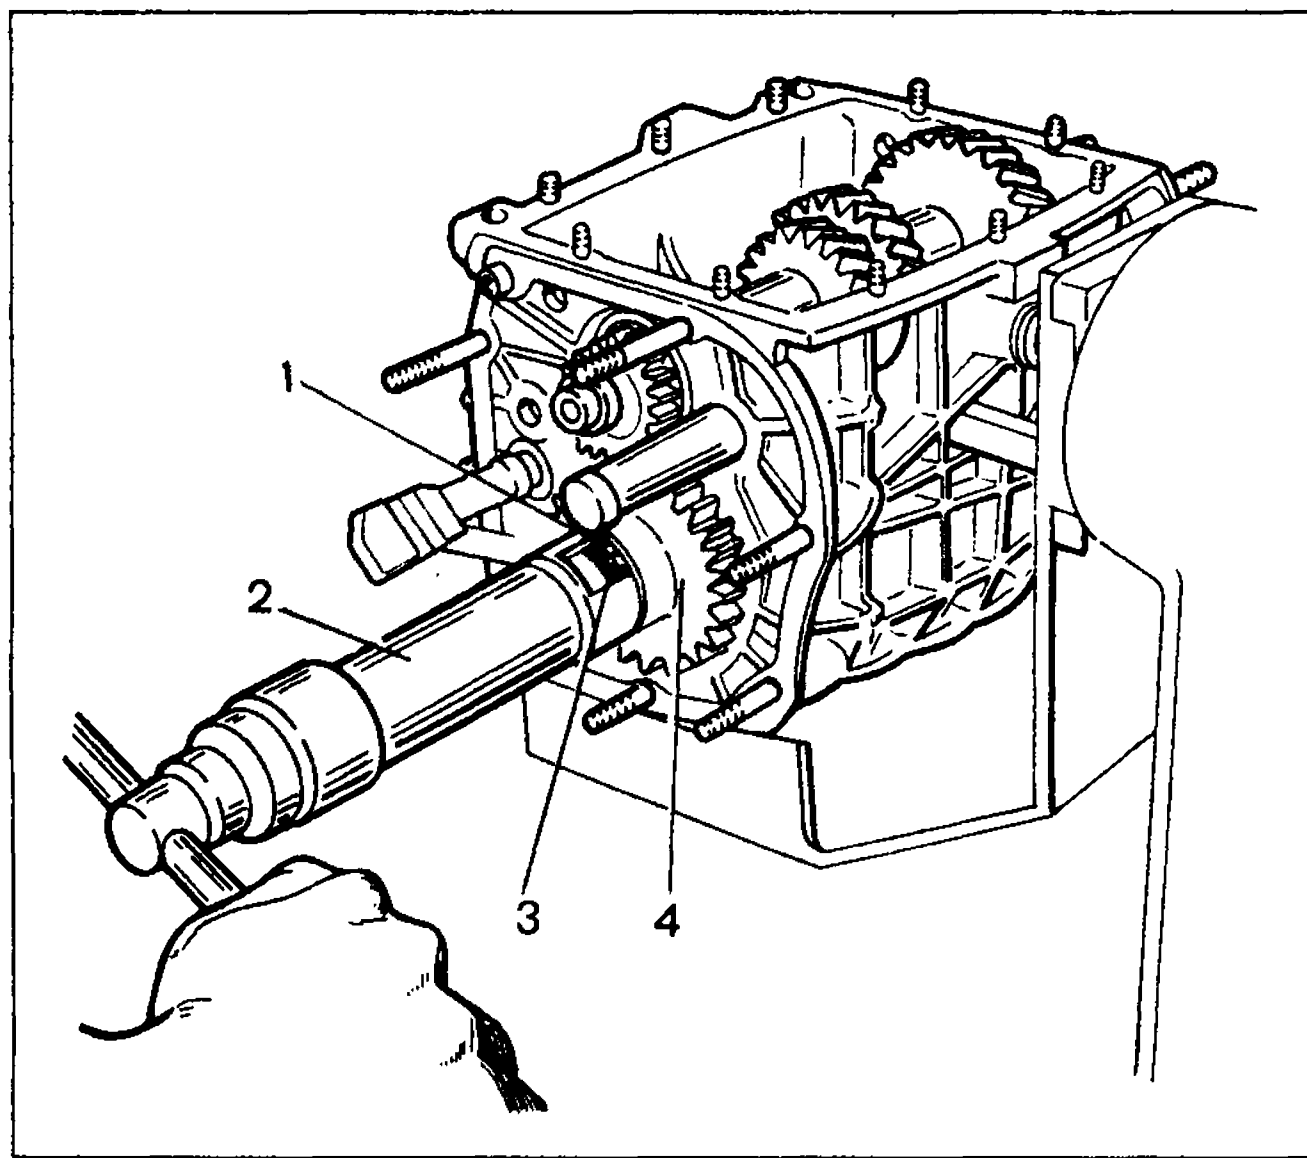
Установка на вторичном валу стопорного кольца шестерни заднего хода:
